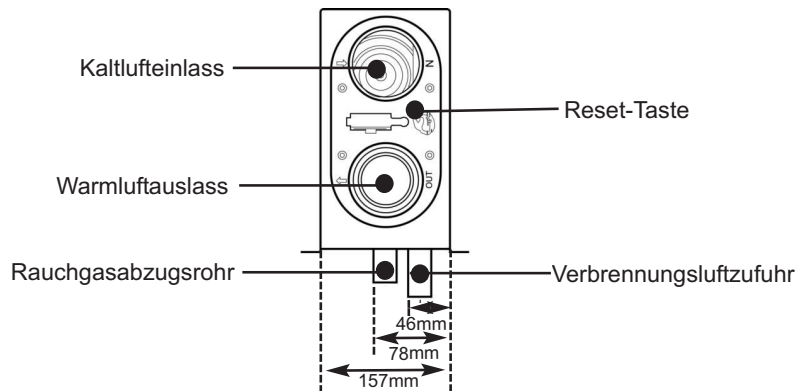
Interne Montage - Frontansicht - SH2202 oder SC2202
